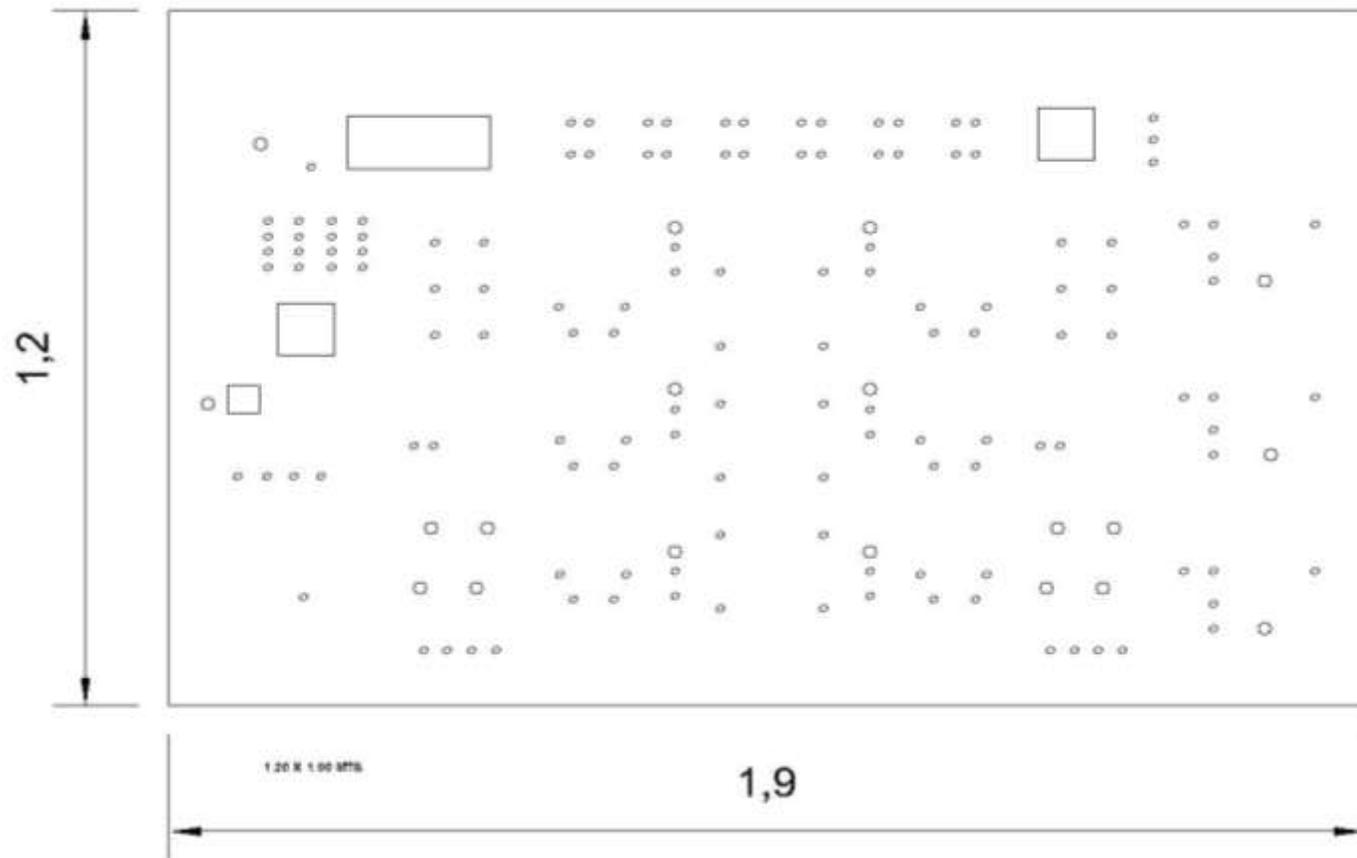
Dimensión de la vista frontal y calado de la estructura del tablero
